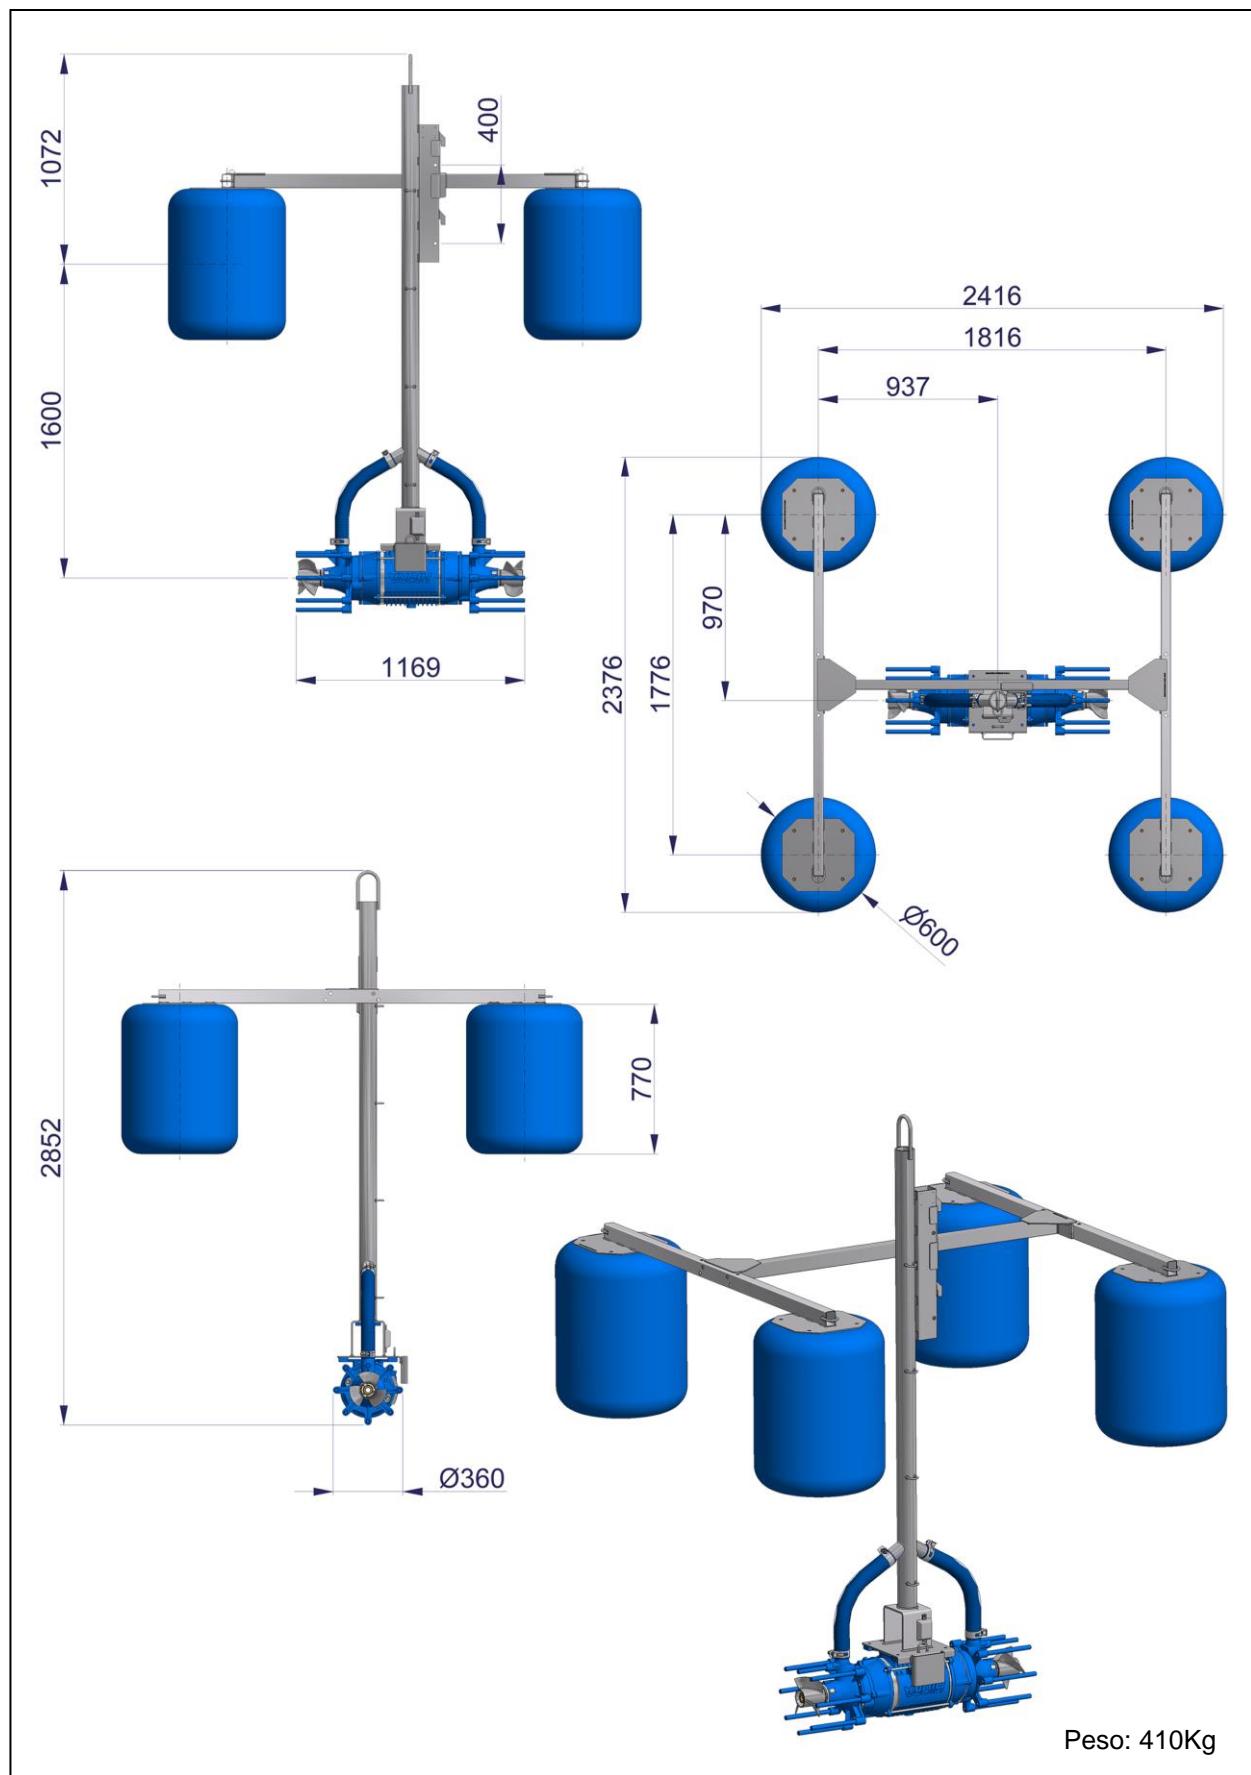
Dimensional TORNADO BITURBO 25,30 e 40CV
